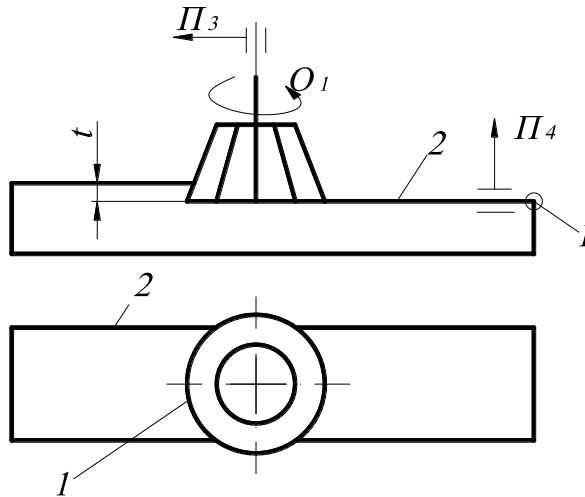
Схема фрезерування площини торцевою фрезою
